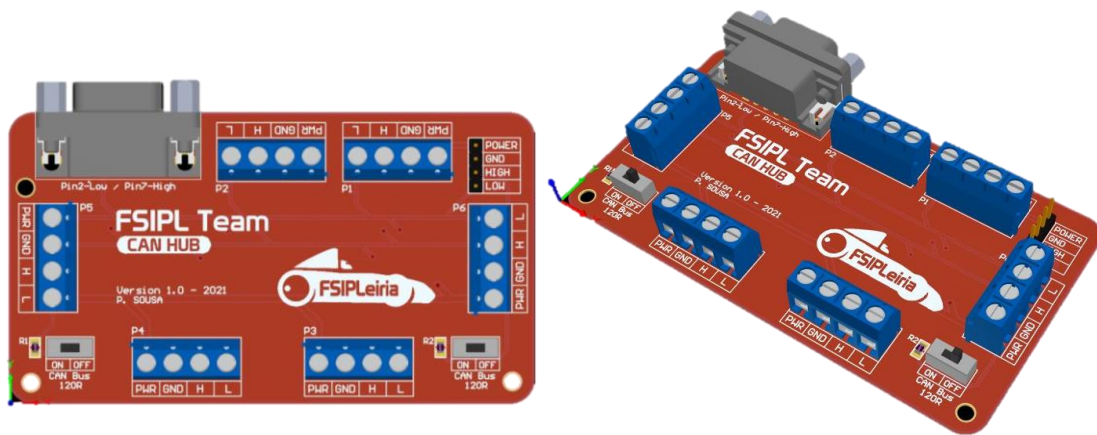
Figura 40 - Design Final da PCB do CANHub - 3D.
